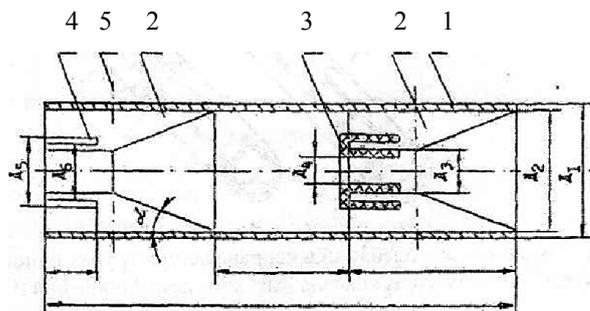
Направляющая труба токарного автомата с демпфирующими металлическими и неметаллическими втулками
